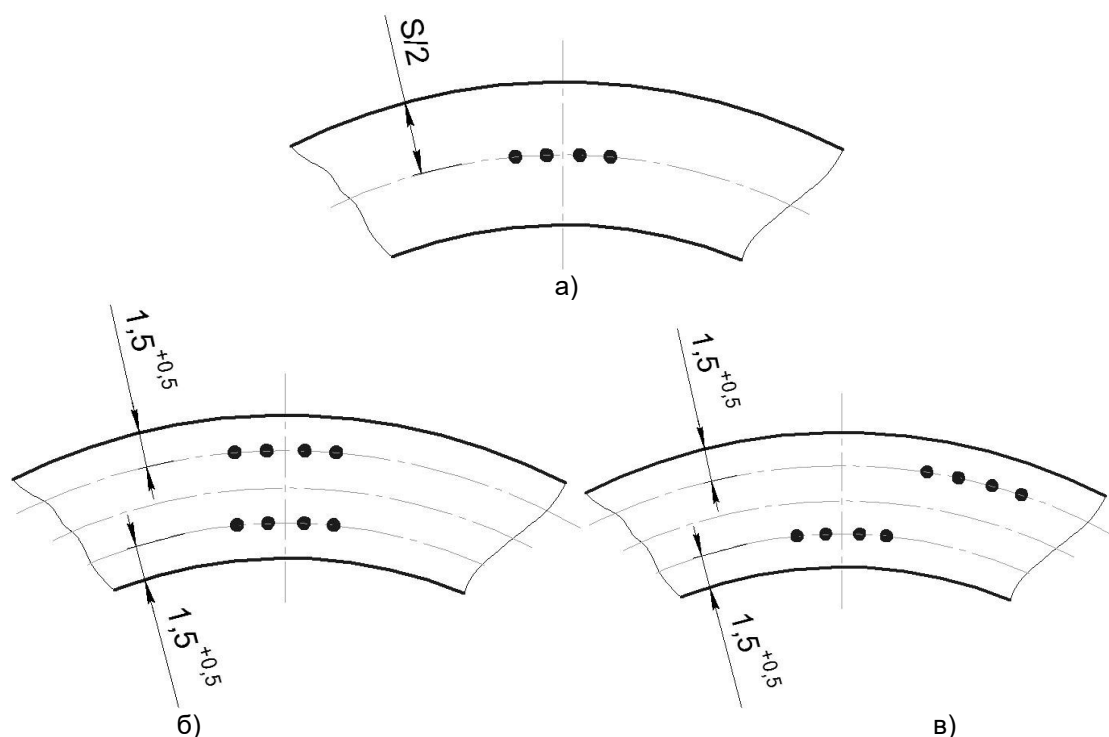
Схема расположения отпечатка при контроле твердости
